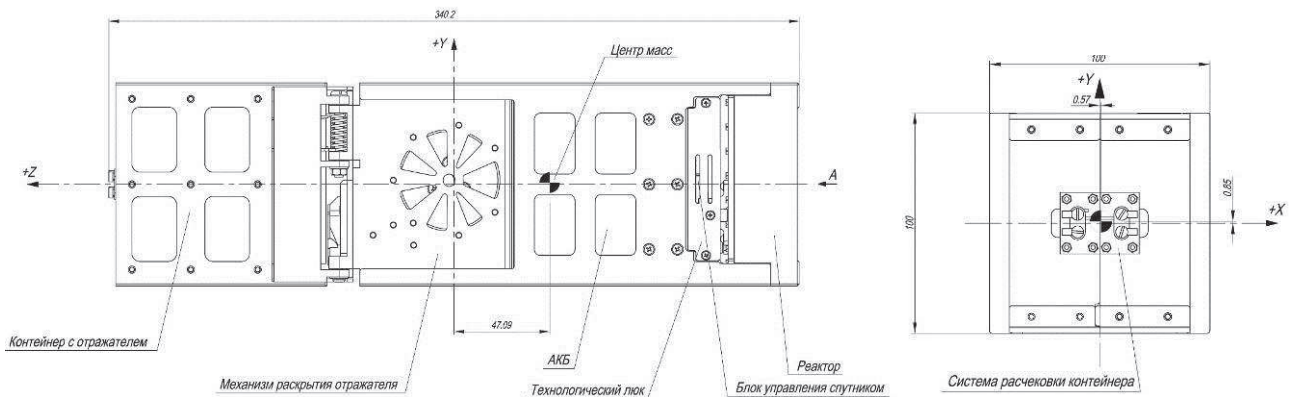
Габаритный чертеж и система координат КА «Маяк»
